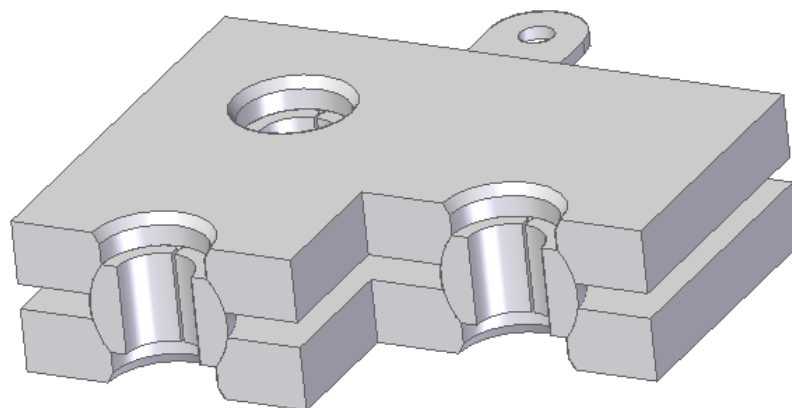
Vista sezionata delle piastre mediane e delle sfere
